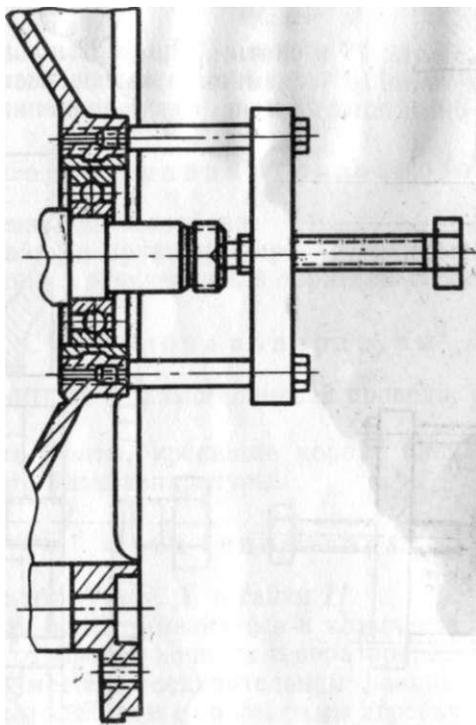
Снятие подшипникового щита со стороны вентилятора
